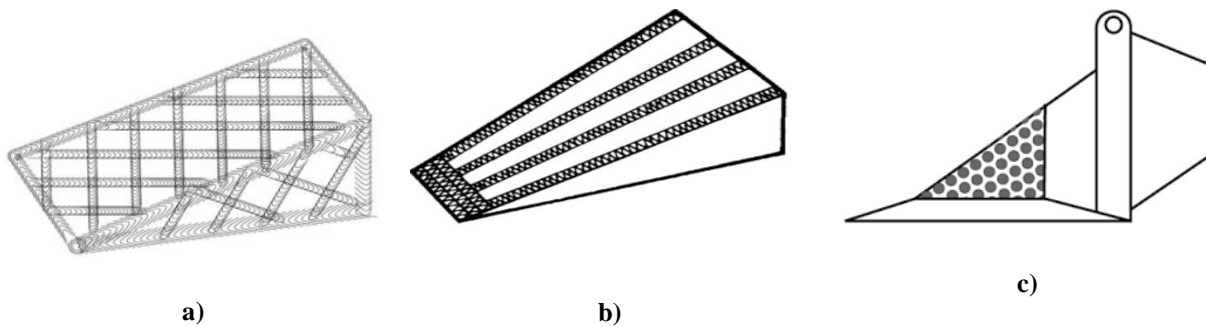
Configuraciones geométricas de la soldadura de blindaje (a)Waffle, (b)Stringer , (c) Dot
